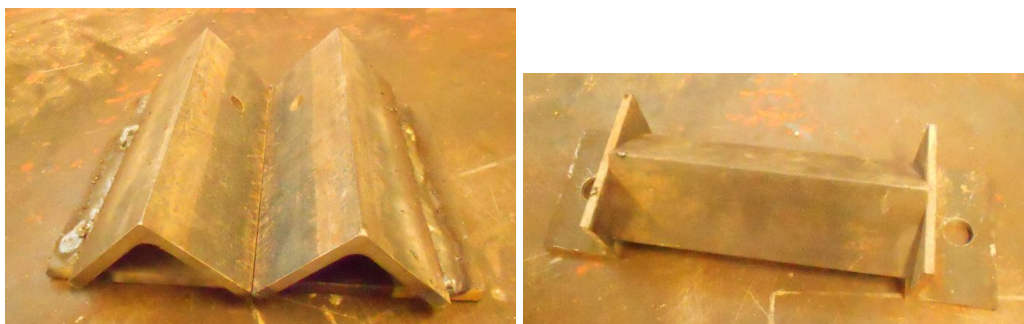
Sistema de sujeción del murete con placa de aplicación de la carga.
